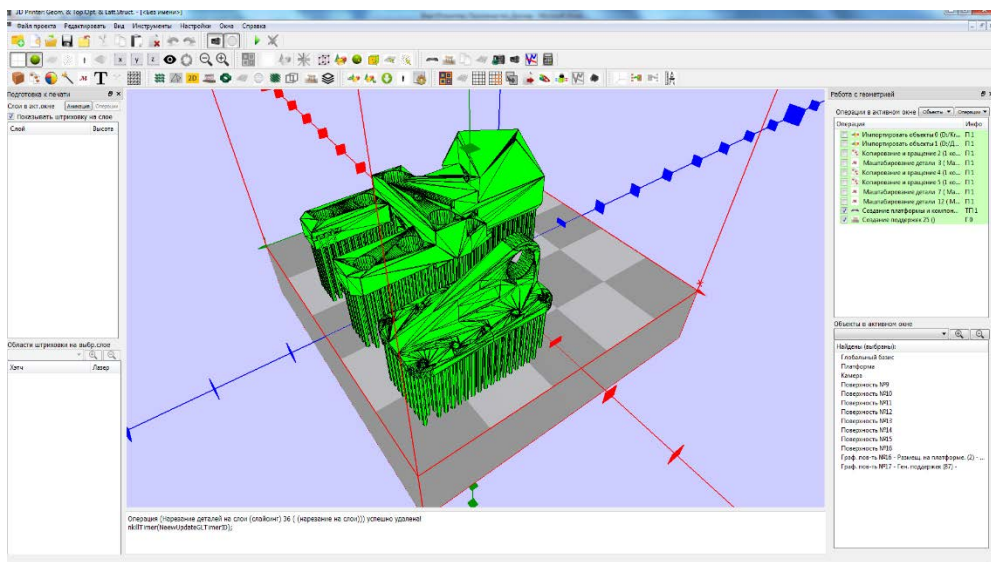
Вид платформы с размещенными на ней деталями и построенными поддержками
